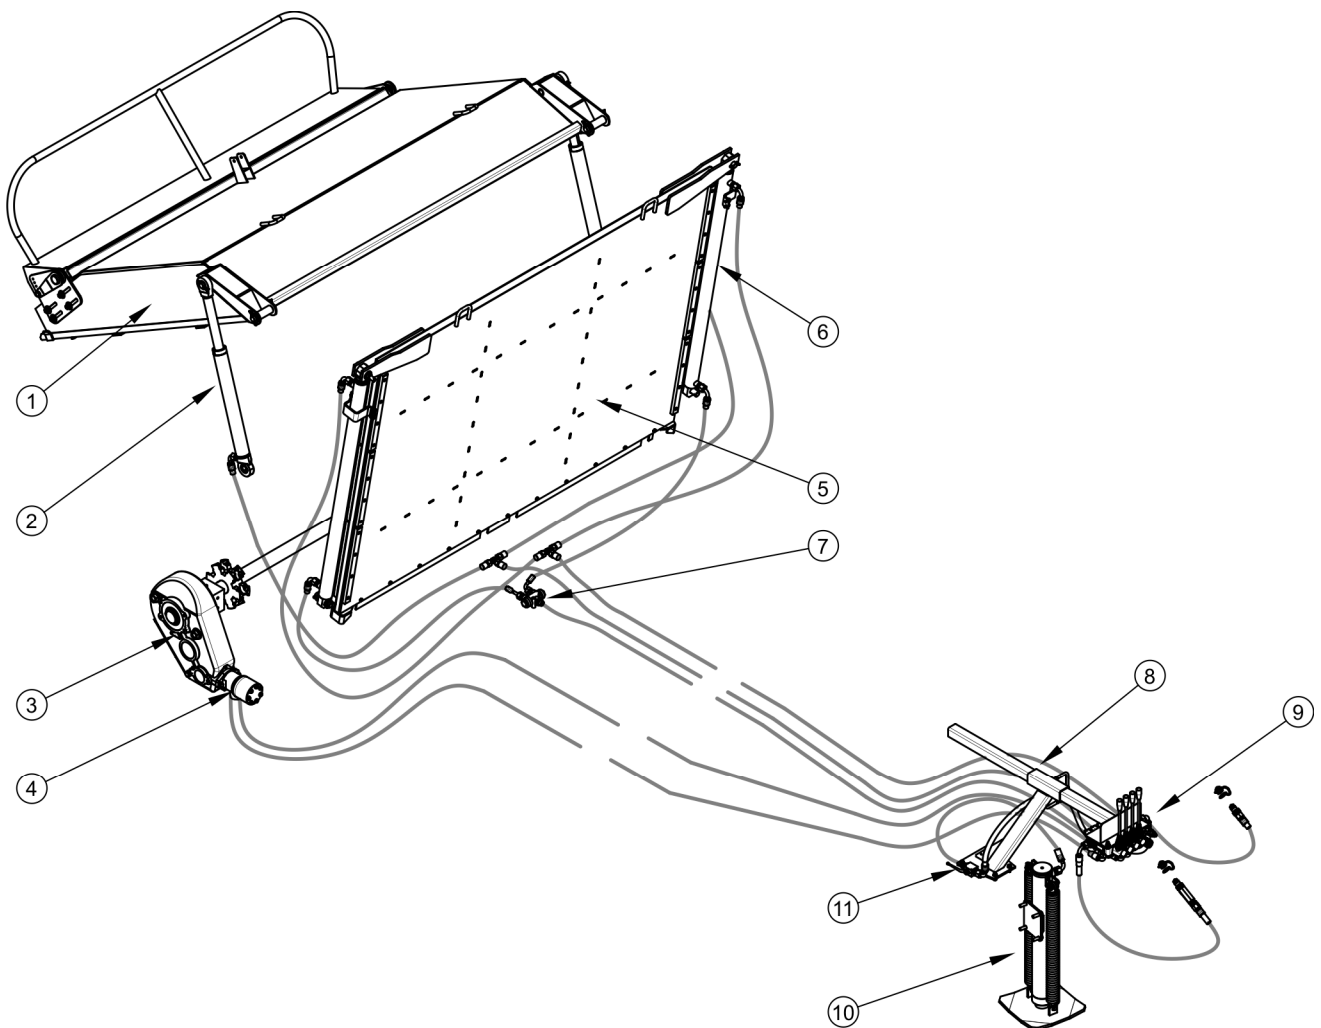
Konstrukce a schéma hydraulické instalace šoupátka
